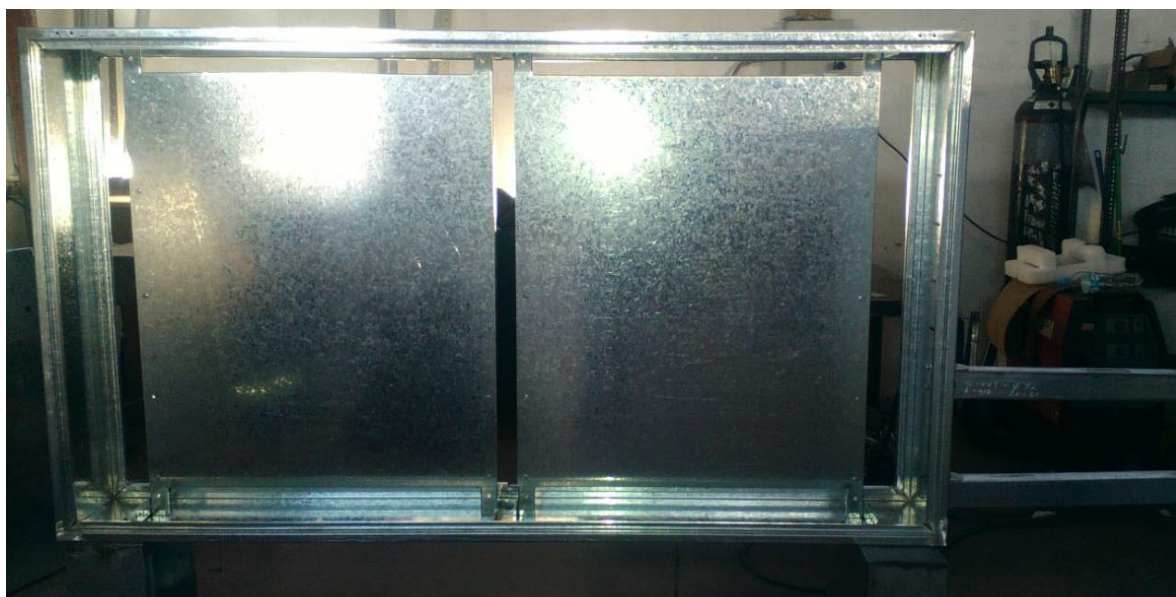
Estructura metálica (marco) Sistema de Entrenamiento
